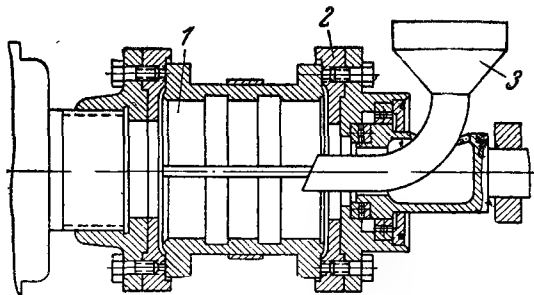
Приспособление к токарному станку для заливки вкладышей.
